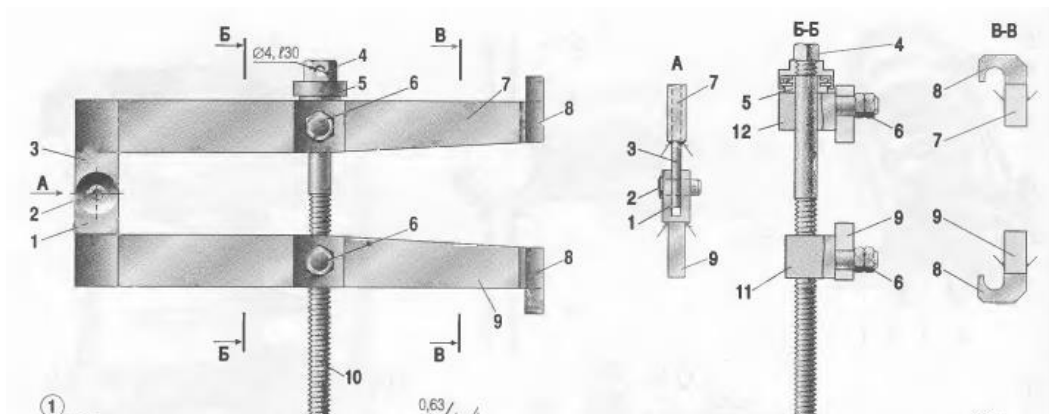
Вид приспособления для сжатия пружин типа «клещи»
